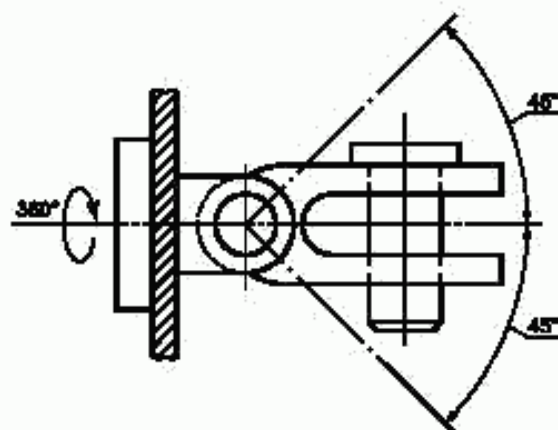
Углы поворота серьги для поворотного сцепного устройства
